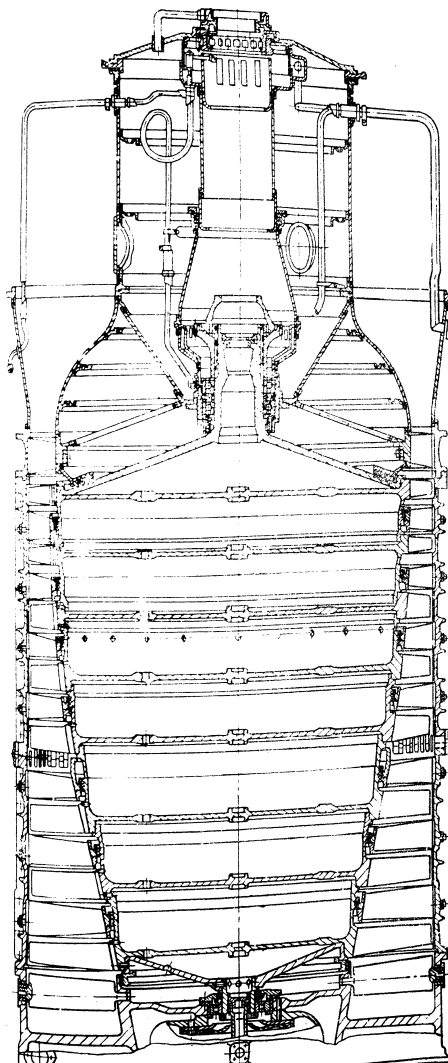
Montáž usměrňovacích lopatek kompresoru.
